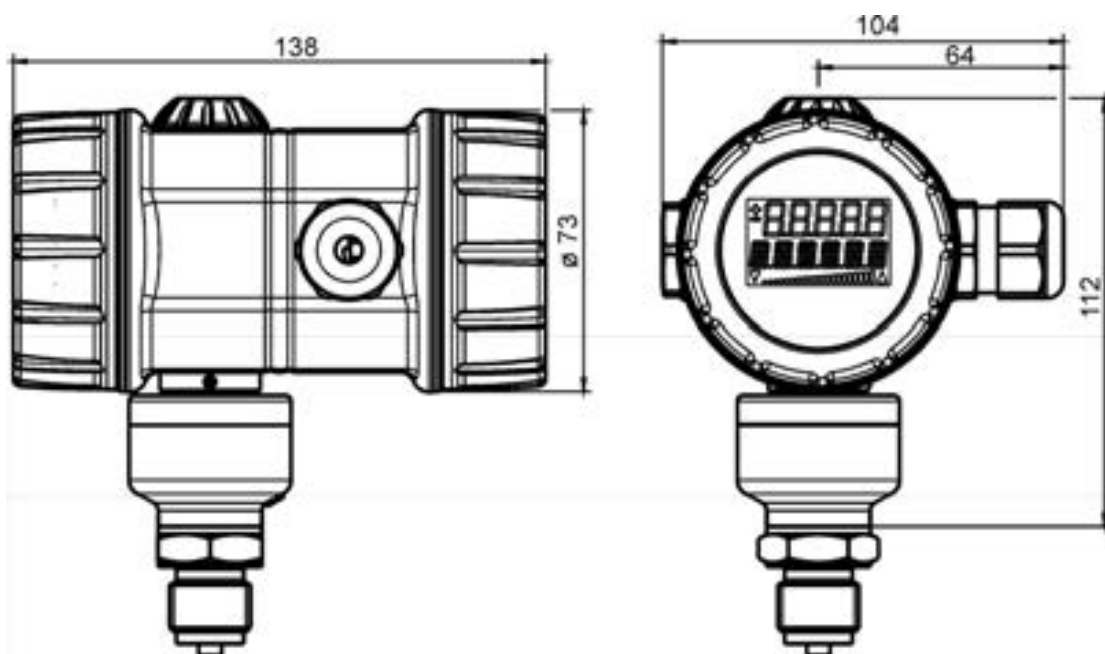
Габаритные размеры преобразователя давления Альбатрос р20 (длинный корпус, нержавеющая сталь, с пластмассовым кабельным вводом)
